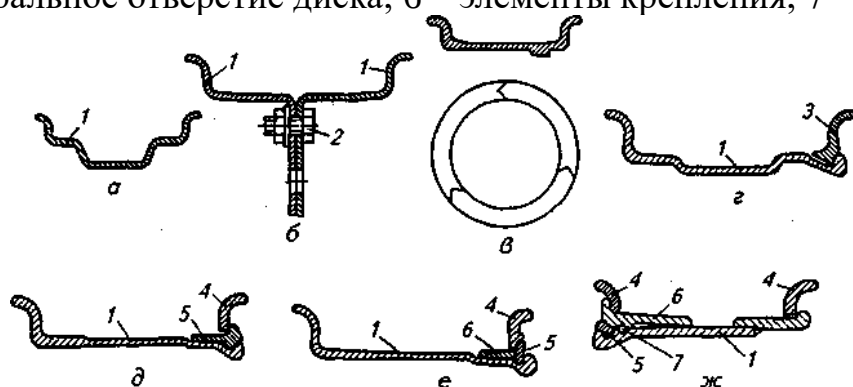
Основные типы ободьев колес: *а* — неразъемный глубокий симметричный; *б* — разъемный посредине; *в* — сегментный типа «трилекс», разделенный по радиусу на три сегмента; *г* — разъемный двухкомпонентный; *д* — разъемный трехкомпонентный; *е* — четырехкомпонентный; *ж* — пятикомпонентный; 1 — основание обода; 2 — соединительный элемент; 3 — разъемное бортовое кольцо; 4 — съемное бортовое кольцо; 5 — пружинное замочное кольцо; 6 — посадочное кольцо; 7 — уплотнитель под бескамерную шину
